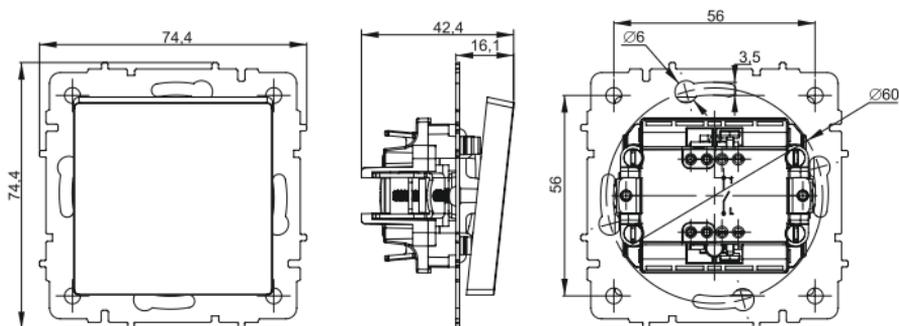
Габаритные и установочные размеры одноклавишного выключателя с безвинтовым зажимом, без рамки / Figure 4 – Overall and mounting dimensions of single-key switch with screwless terminal, without frame / 4-сურет – бұрандасыз қысқышы бар, жақтаусыз бір кілтті қосқыштың жалпы және орнату өлшемдері / Figura 4 – dimensiunile de gabarit și de instalare ale întrerupătorului cu o cheie cu demă fără șuruburi, fără cadru / ნახატი 4 – ერთკლავიანი ამომრთველის გაბარიტული და საყენებელი ზომები, უხრანო მომჭერით, ჩარჩოს გარეშე / 4-сურет – бир ачыктуу өчүргүчтүн жалпы жана монтаждык өлчөмдөрү, рамкасыз, бурагы жок кыскыч менен / Тасвири 4 – Андозаҳои габаритӣ ва васлкунии калидаки ятғумгаӣ бо исканҷаи бепеч, бе чорқуба / 4-rasm – Ramkasiz, vintsiz qisqichli bir klavishali viklyuchatelning gabarit va o'rnatish o'lchamlari
